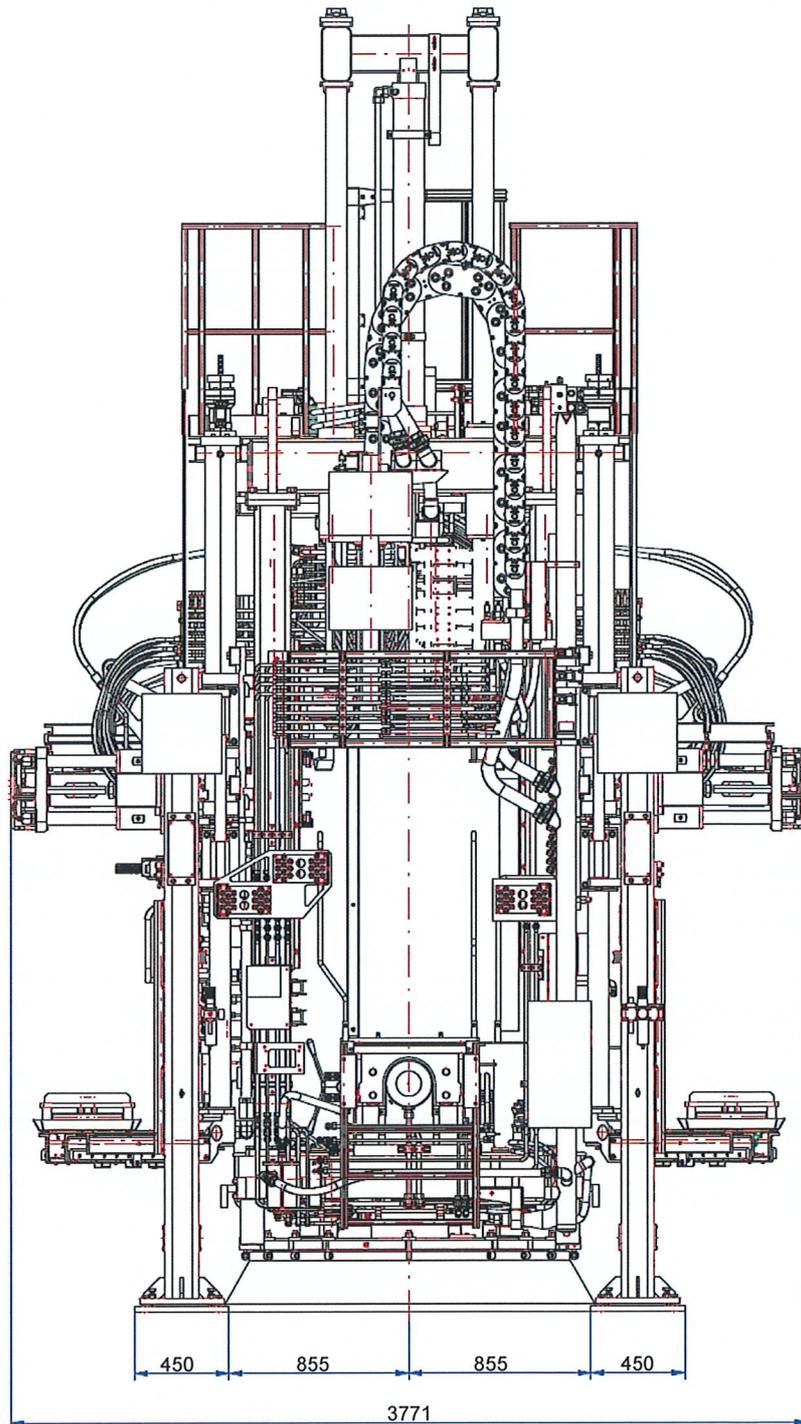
Maschinenlayout mit Gußteilentnahme - Seitenansicht
